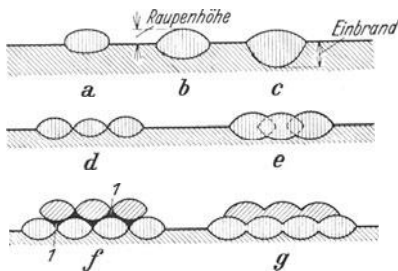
Querschnitte durch Schweißraupen.
